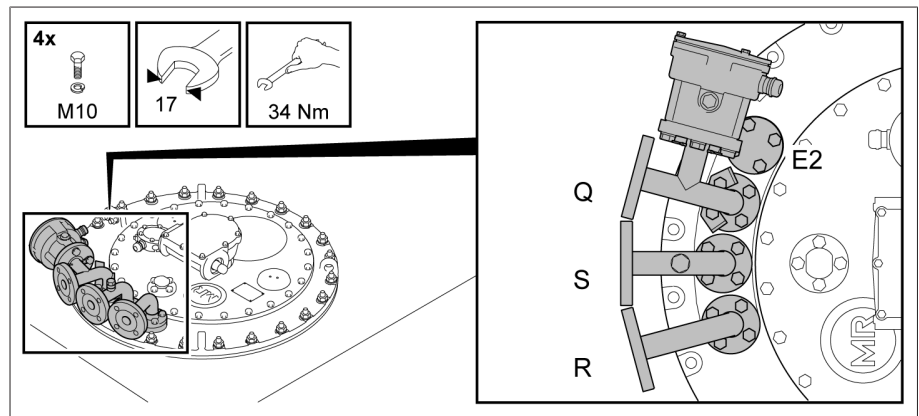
Rohrleitungsanschlüsse mit Rohrleitungsbögen
